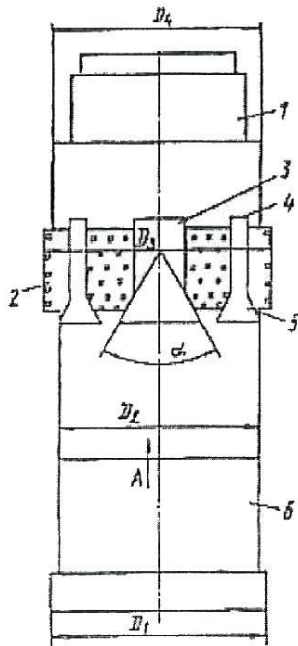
Алмазный расширитель: 1-корпус; 2- алмазосодержащий штабик; 3-промывочный канал; 4-выходная кромка; 5- входная кромка; 6- корпус коронки
